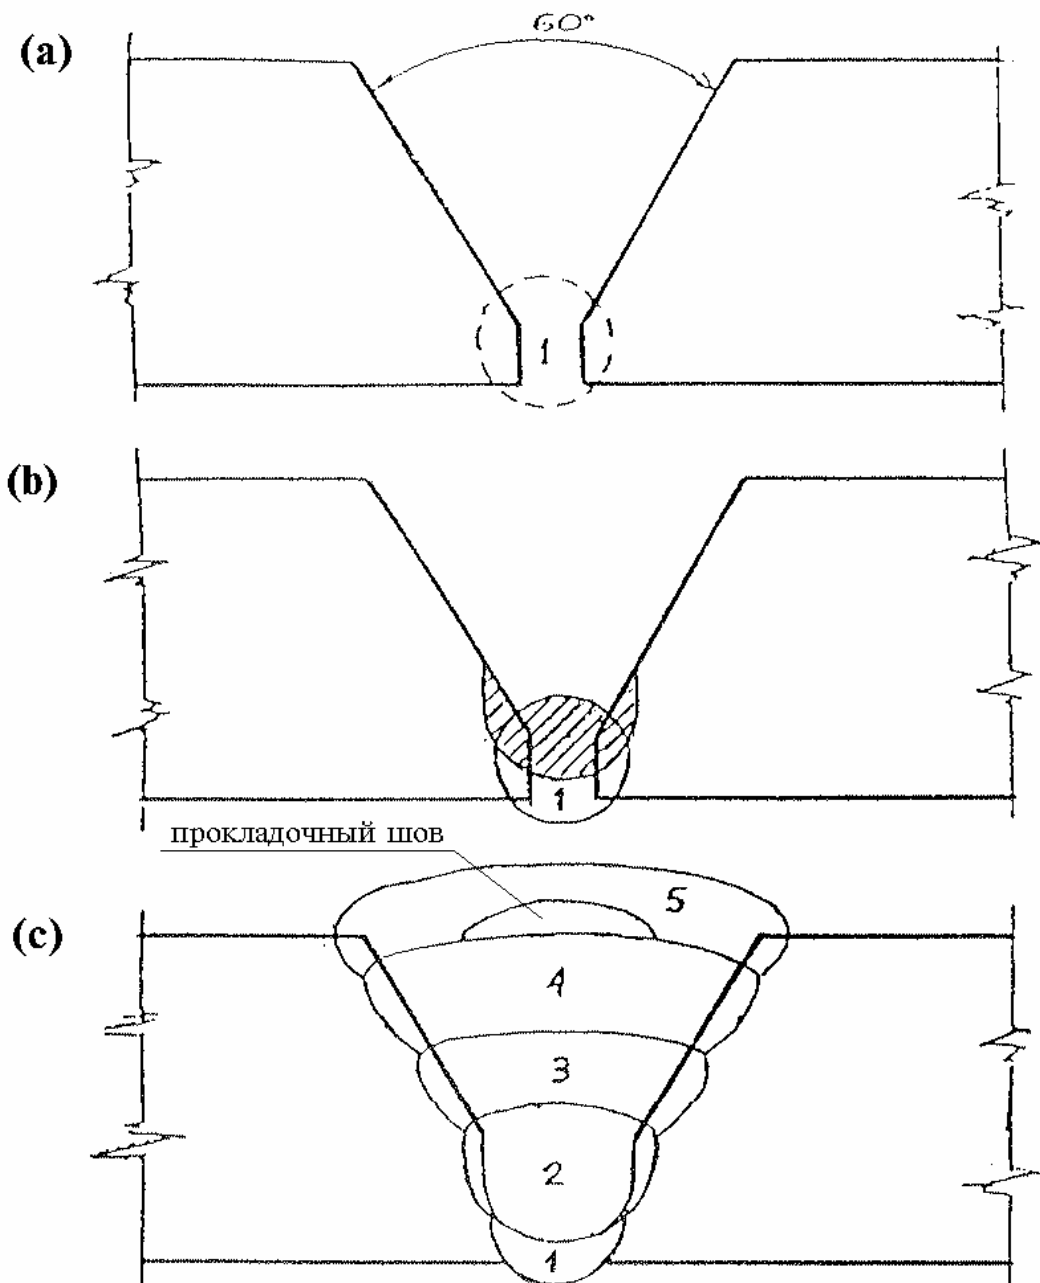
Шлаковые включения, образующиеся по краям корневого шва при сварке штучными электродами с целлюлозным покрытием. Недостаточно тщательная зачистка корневого шва может повлечь возникновение сварочных дефектов - "карманов" - при выполнении горячего прохода электродами того же типа.
